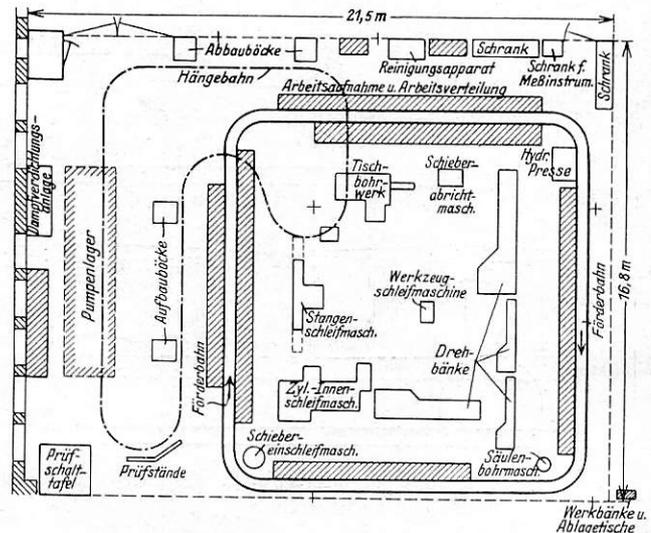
Grundriß der Pumpenwerkstätte im Werk München.
